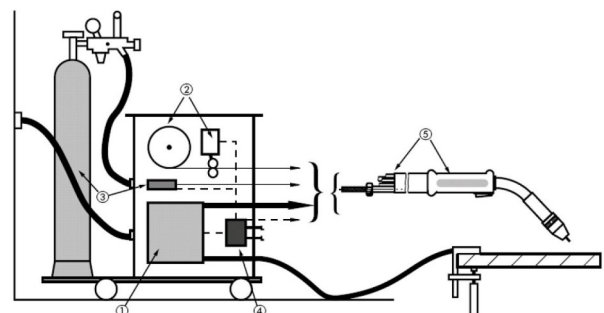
Funktionsprinzip des Schweißgeräts
